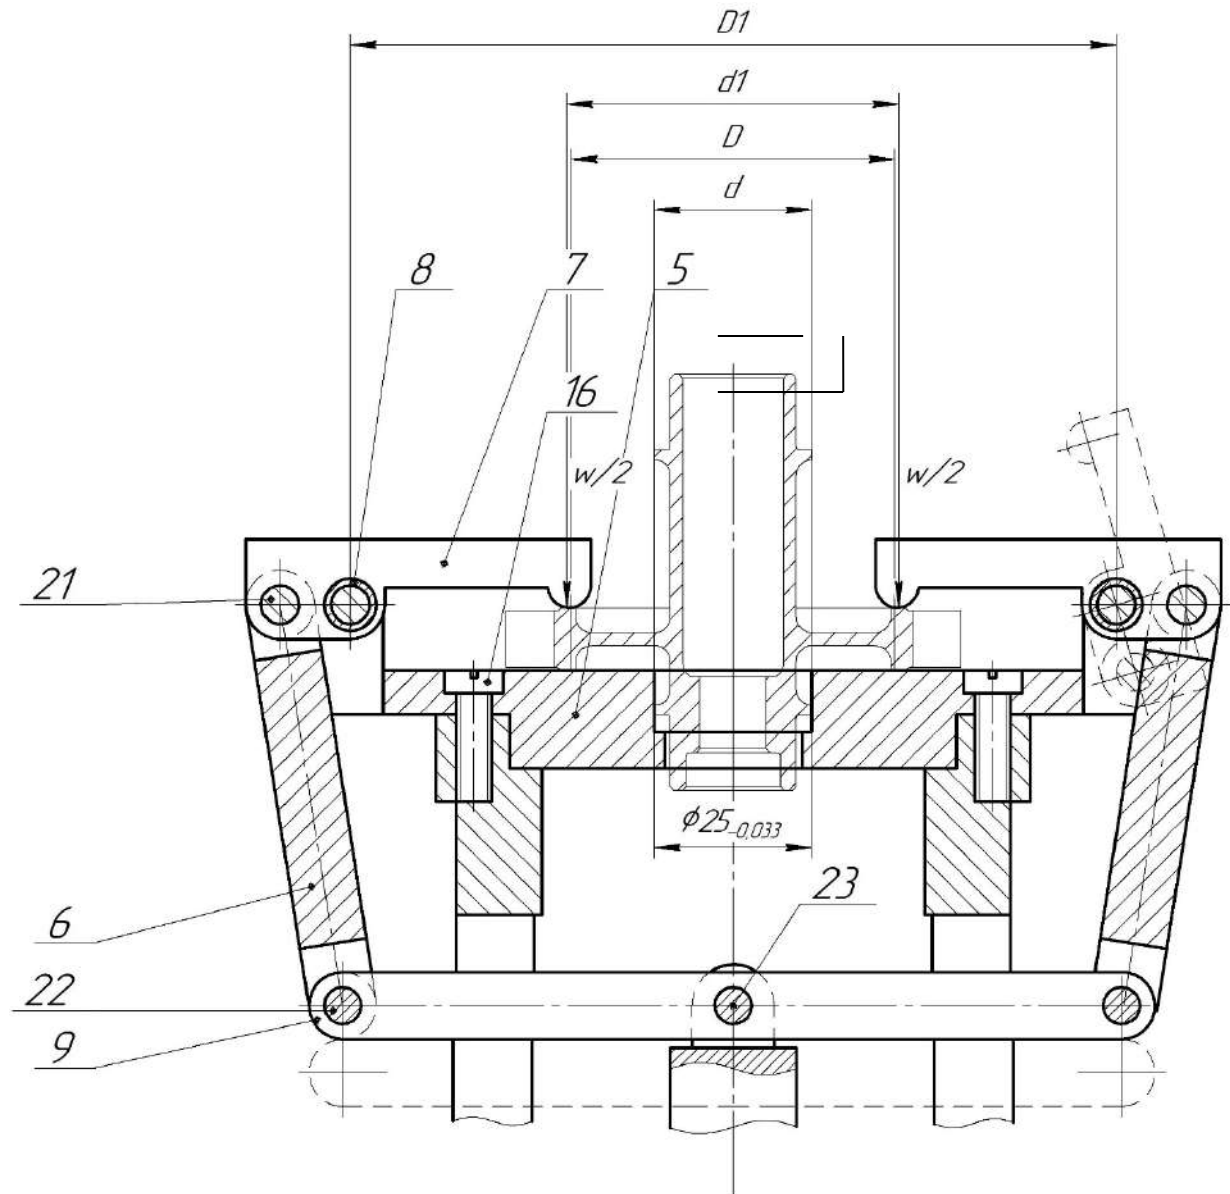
Схема для визначення зусилля закріплення у фрезерному пристосуванні
